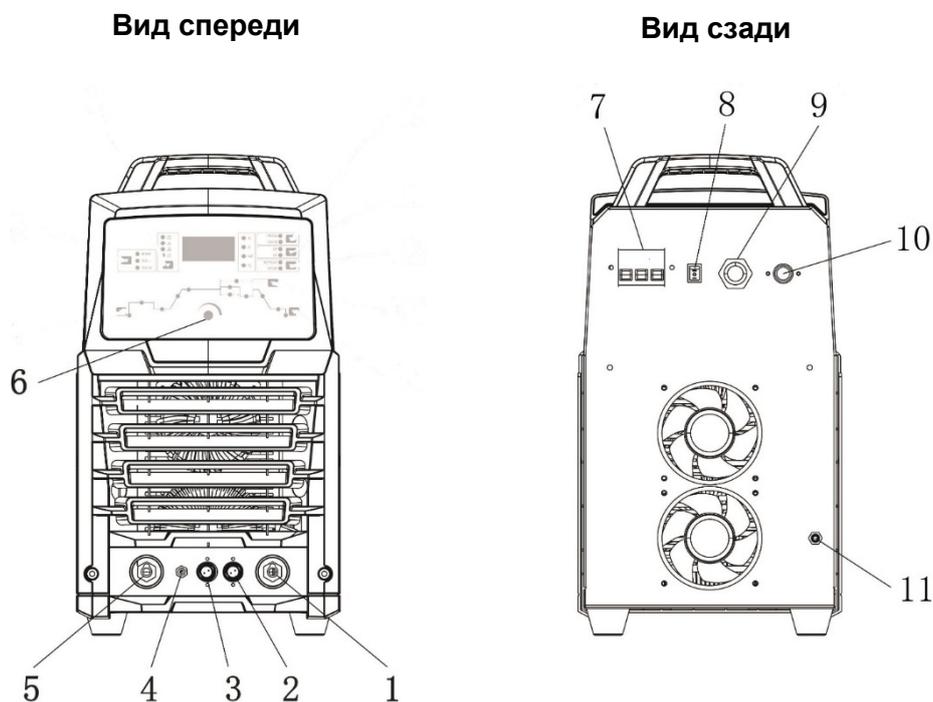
Общий вид (Инверторный сварочный аппарат постоянного тока MMA)
